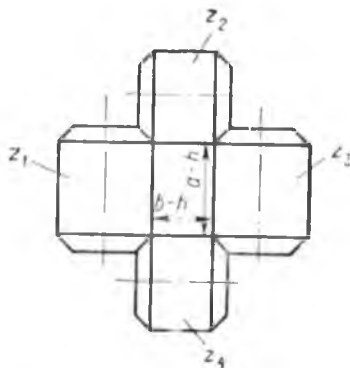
Фальер из зубчатых колес для гофрирования
